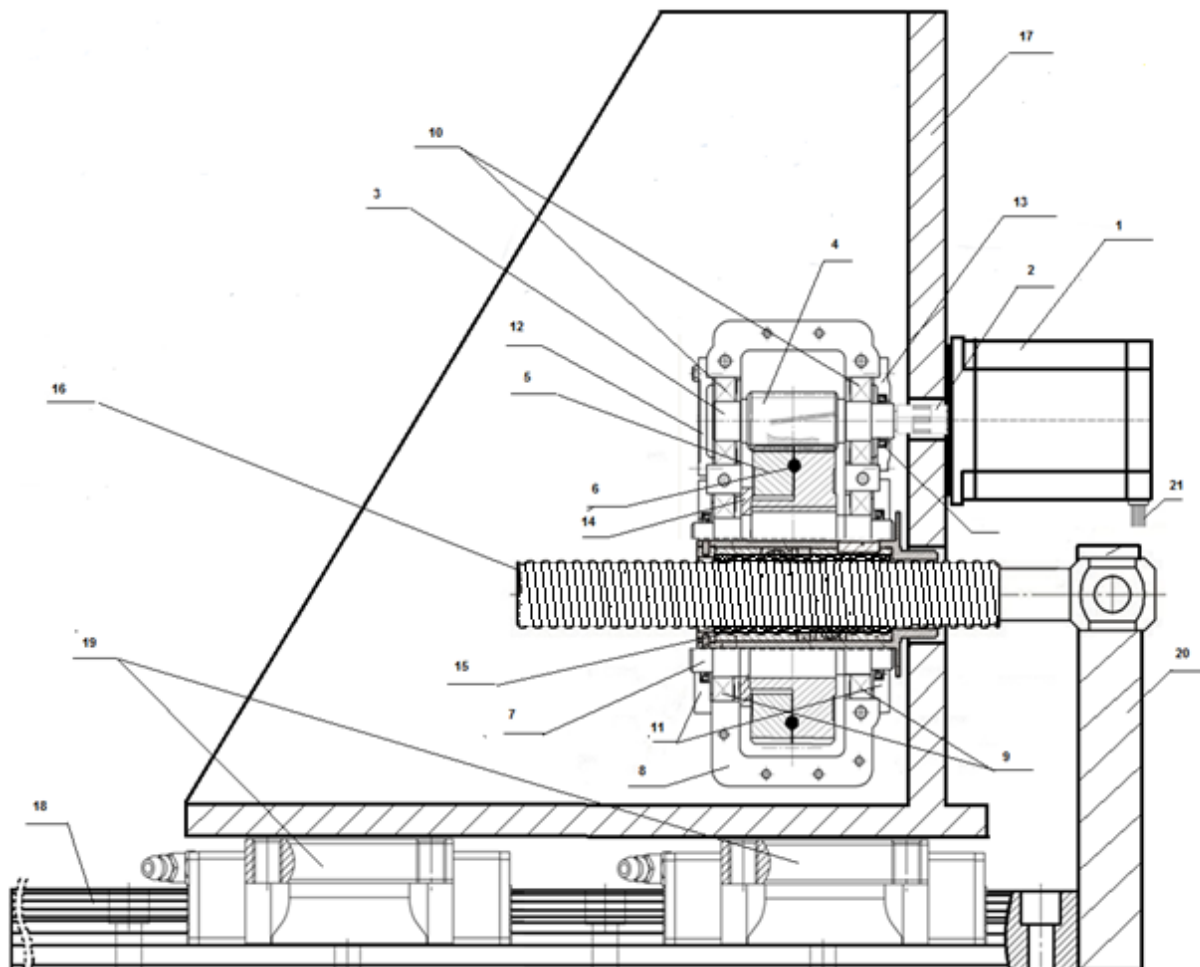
Проектный чертеж ПЛП: 1 – шаговый двигатель; 2 – жесткая муфта; 3 – быстроходный вал редуктора; 4 – шестерня быстроходного вала; 5 – разрезное зубчатое колесо; 6 – люфтовывбирающее устройство; 7 – тихоходный вал; 8 – корпус редуктора; 9 – радиально-упорные подшипники; 10 – радиальные подшипники; 11 – крышки подшипников тихоходного вала; 12 – крышка подшипника быстроходного вала; 13 – крышка быстроходного вала; 14 – упорное кольцо; 15 – гайка РВП; 16 – винт РВП; 17 – рама портала; 18 – рельсовая направляющая; 19 – каретки; 20 – жесткие опоры ходового винта; 21 – кабель питания и управления шаговым двигателем
